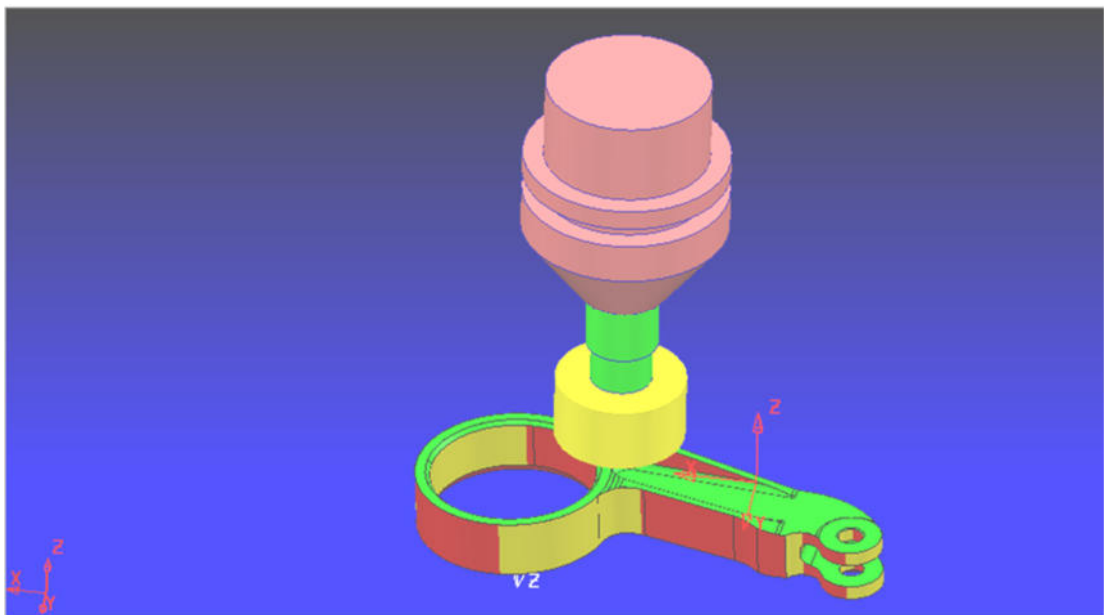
Фрезерування торцевою фрезою поверхні - 4,
